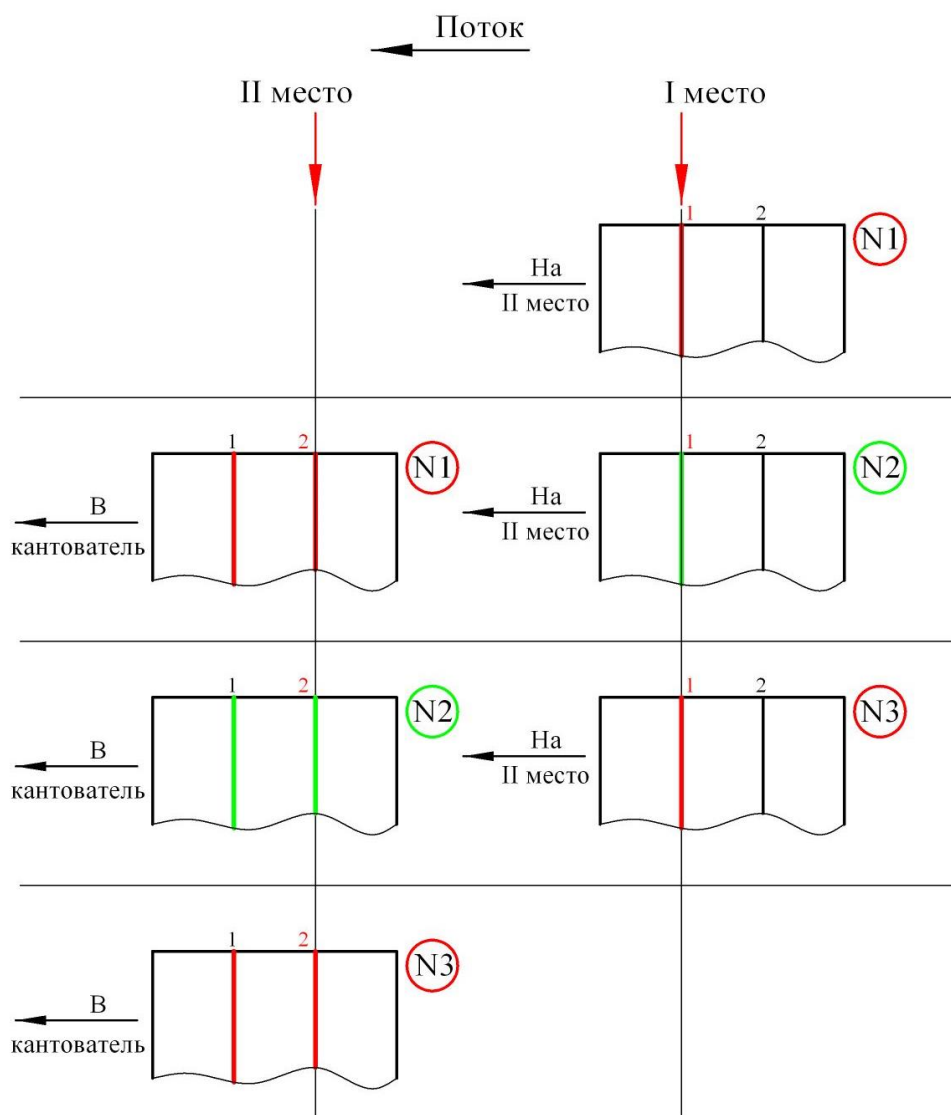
Схема сварки на двухместном стенде двух стыковых листовых полотнищ:
